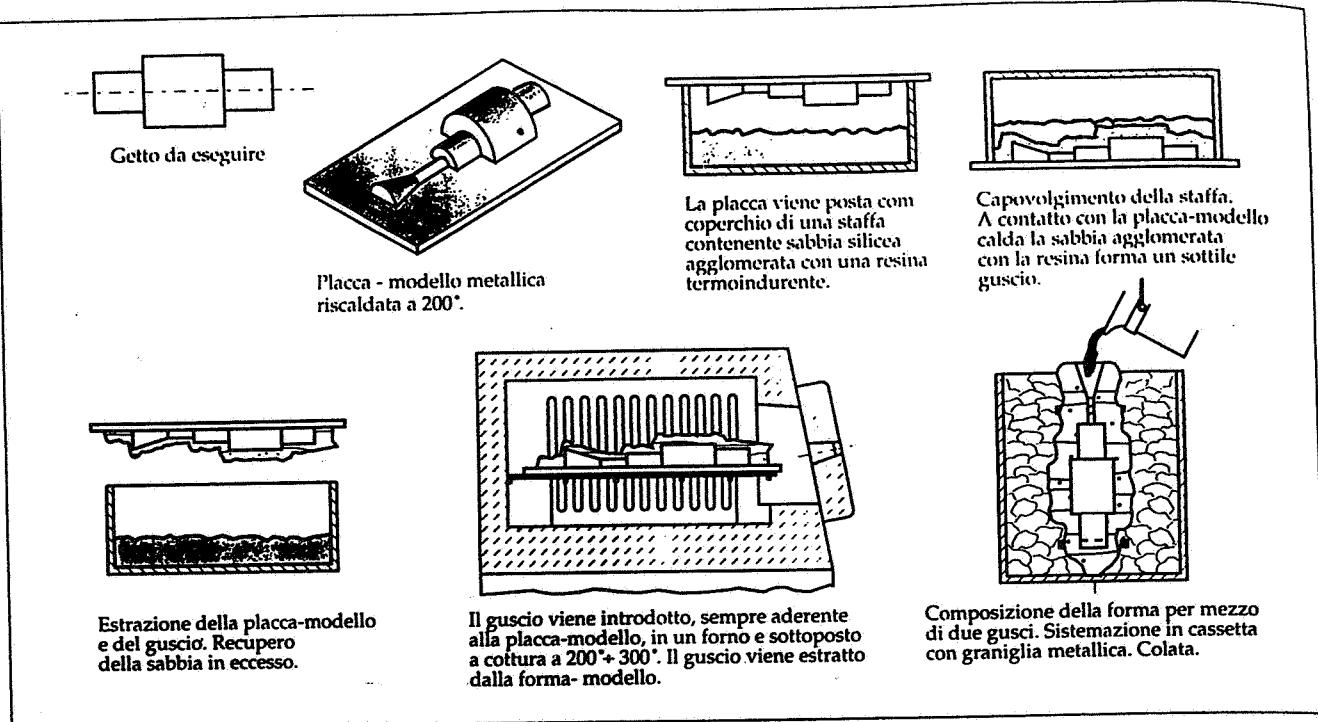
Le diverse fasi della formatura a guscio (shell-molding).
